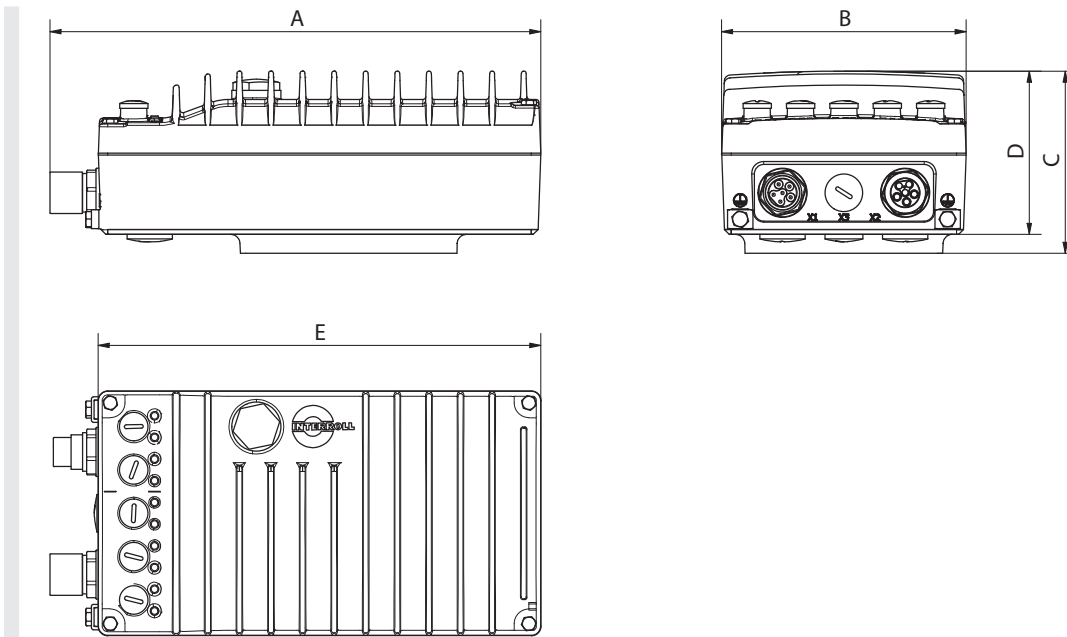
, montaje en motor, tamaño constructivo 1 y 2
